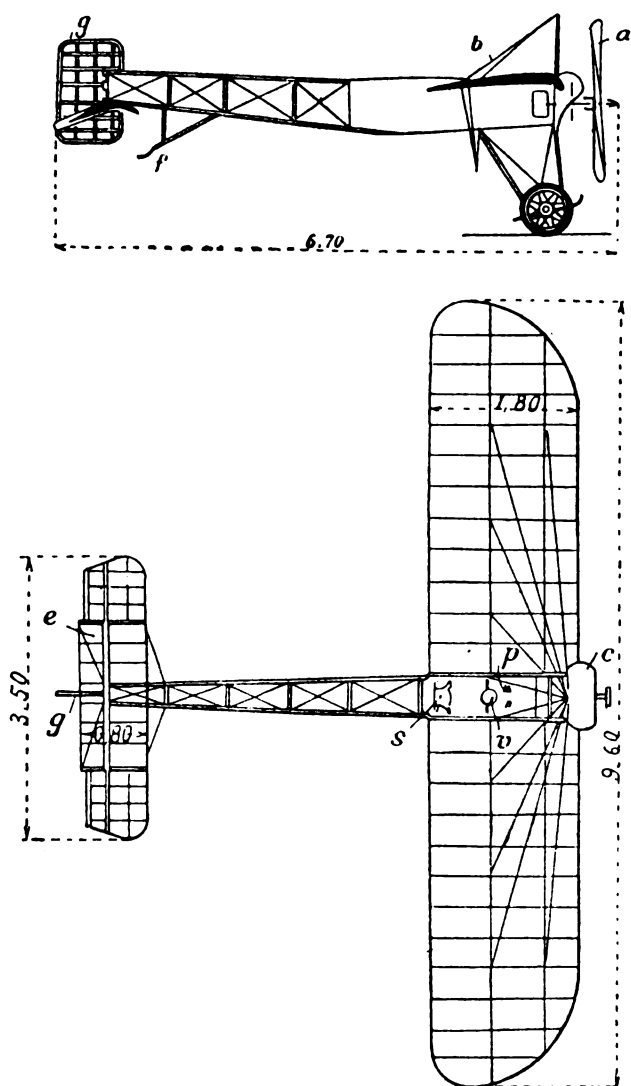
Monoplano Morane - Elevazione e pianta.
